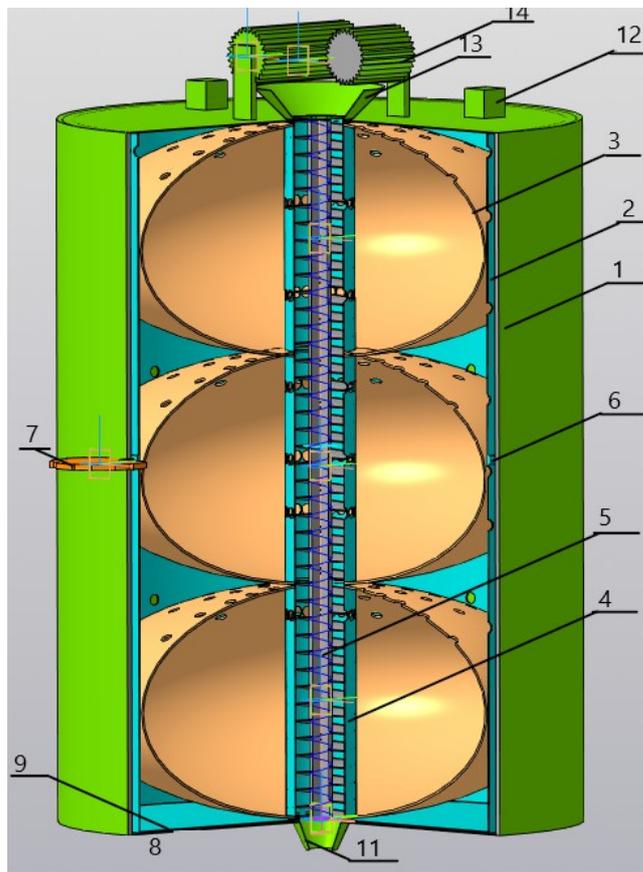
Размораживатель молозива животных непрерывно-поточного действия с СВЧ энергоподводом в коаксиальный резонатор
